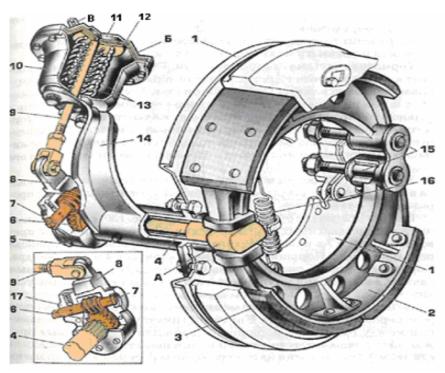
Рабочий тормозной механизм автомобиля ЗИЛ;
